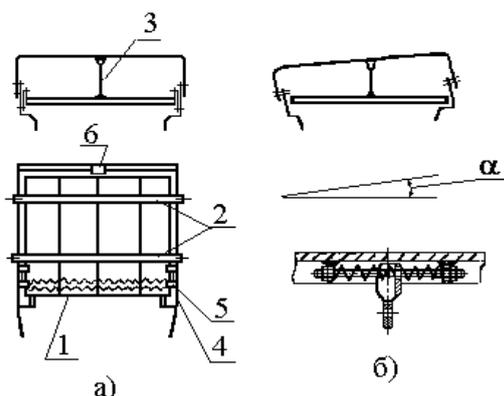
Верхний решетный стан с самоустанавливающимся решетом: а – вид стана; б – выравнивающий механизм; 1 - жалюзийное решето; 2 - поперечные балки; 3 - подвеска; 4 - каркас стана; 5 - боковые упоры; 6 - центральный упор
